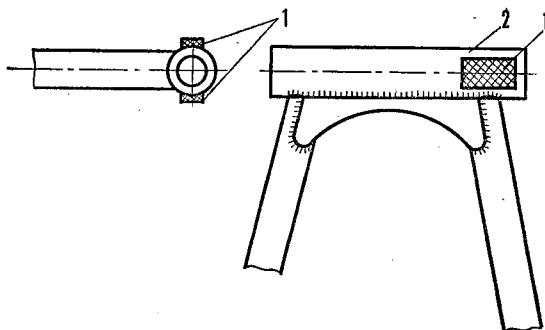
Установка предохранительных накладок: 1 — накладки; 2 — труба для оси вилки
